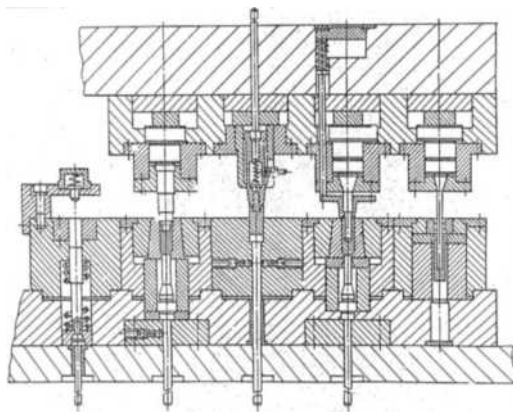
Пример конструкции многопозиционного штампа с линейным расположением инструмента для штамповки деталей типа стакана
